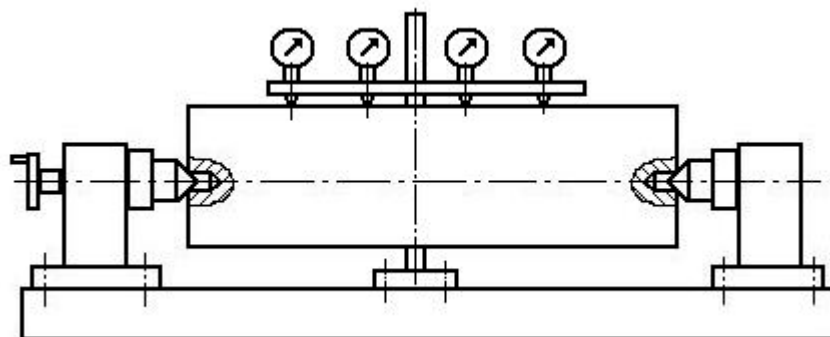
Схема измерения линейного съёма металла с поверхности валика
